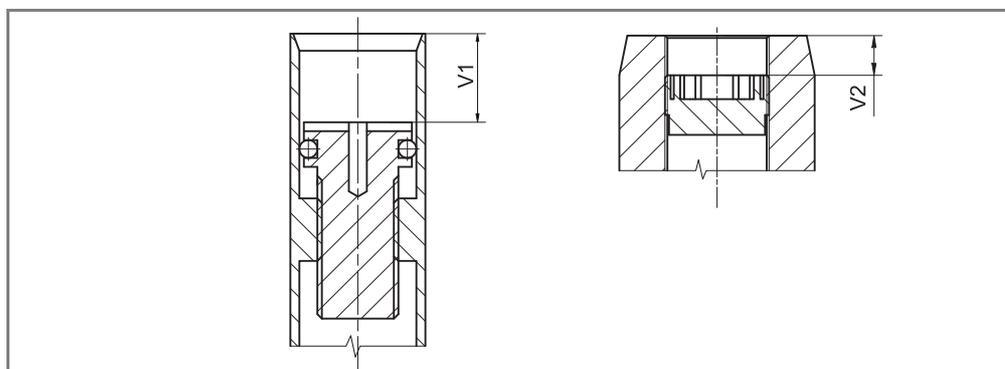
Tiefe der Ventilschrauben V1 und V2
